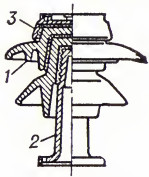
Опорный штыревой изолятор высокого напряжения: 1 — фарфоровая часть; 2 — штырь; 3 — шапка.
